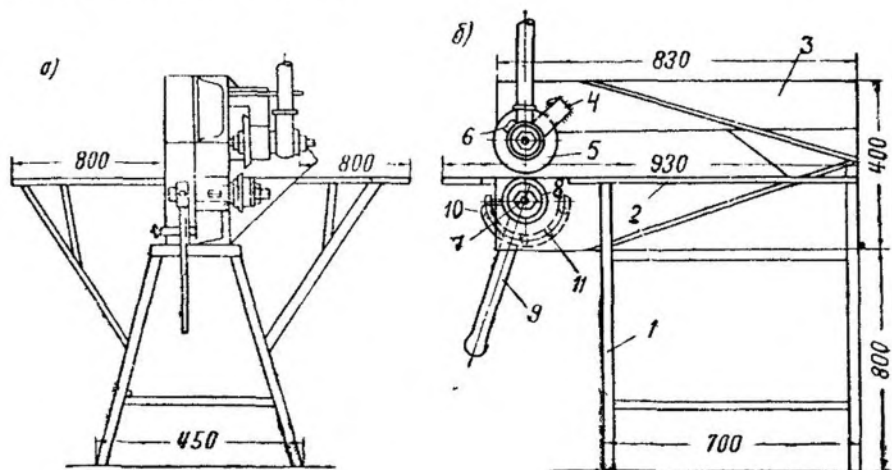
Ручной станок для внутренних вырезов в листовой стали
